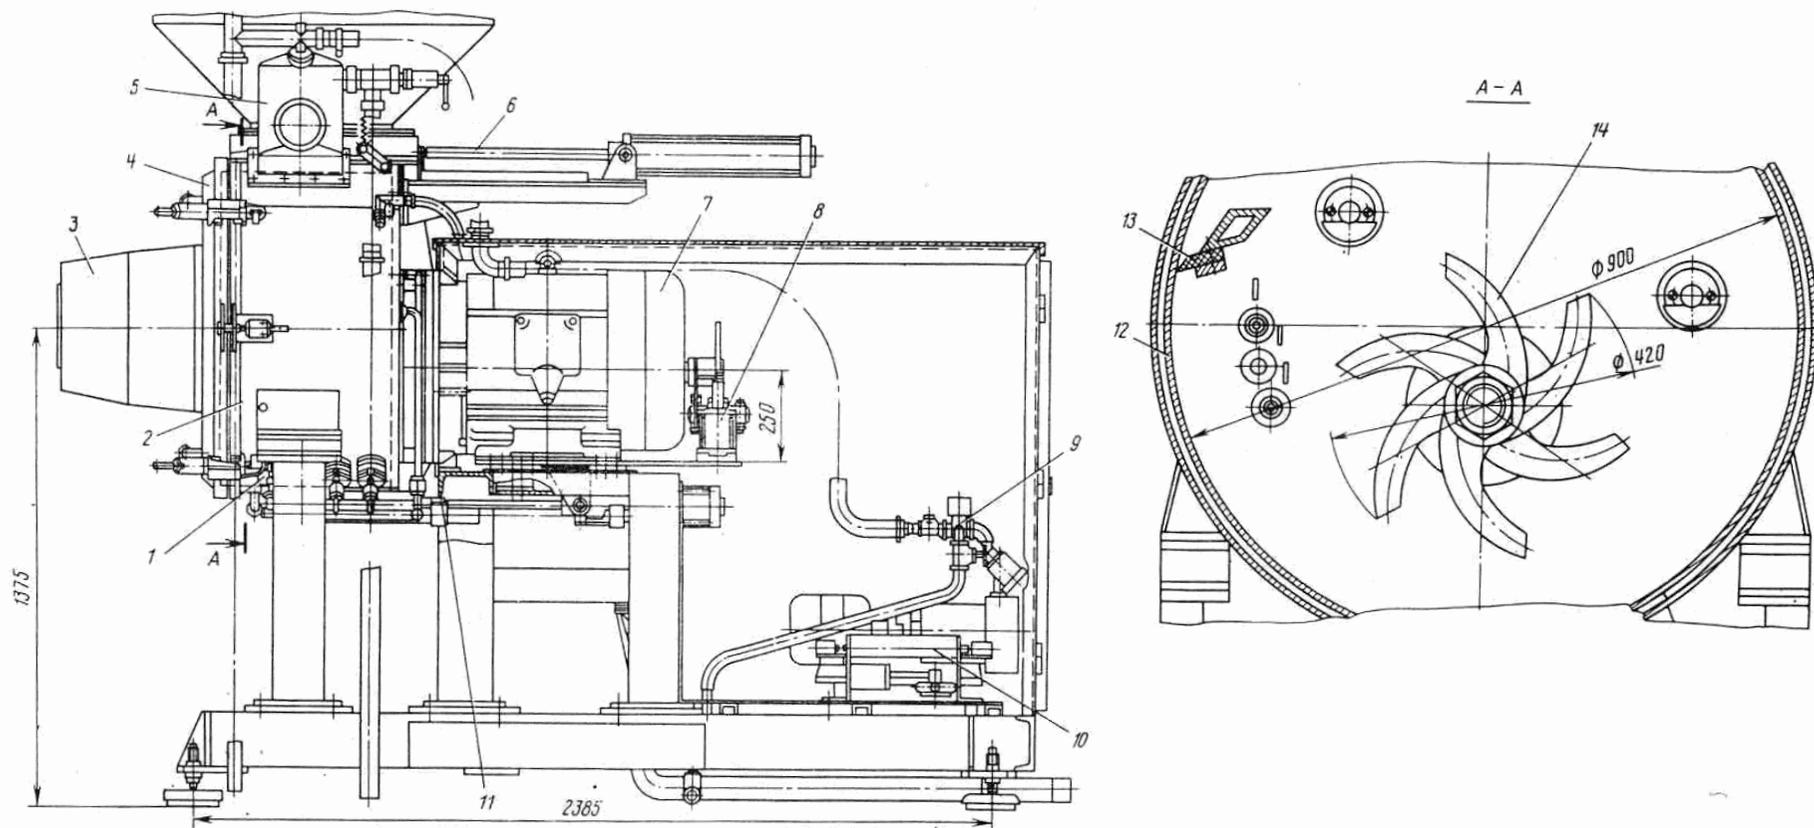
Агрегат для измельчения сыра и плавления сырной массы: 1 – клапан обратный; 2 – барабан; 3 – привод; 4 – крышка; 5, 9 – вакуумная система; 6 – загрузочный шибер; 7 – двигатель; 8 – тормоз; 10 – дозатор; 11 – разгрузочный шибер; 12 – рубашка охлаждения; 13 – мешалка; 14 – нож
